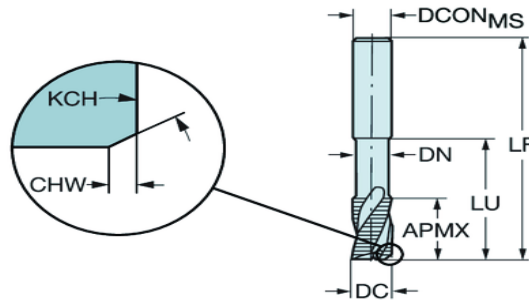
Фреза R216.33-25040-AJ25U H10F
